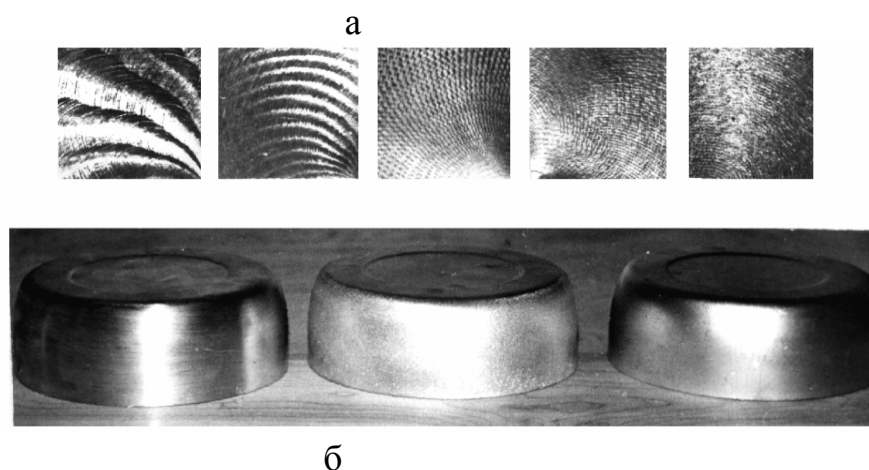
Фотографии макрорельефа (а) поверхности образцов из алюминиевых сплавов марки АмГЗ после различных режимов обработки: 1 - 250 об/мин; 2 - 325 об/мин; 3 - 410 об/мин; 4 - 630 об/мин; 5 - 840 об/мин; вид поверхности деталей после иглофрезерования и абразивной обработки (б).
